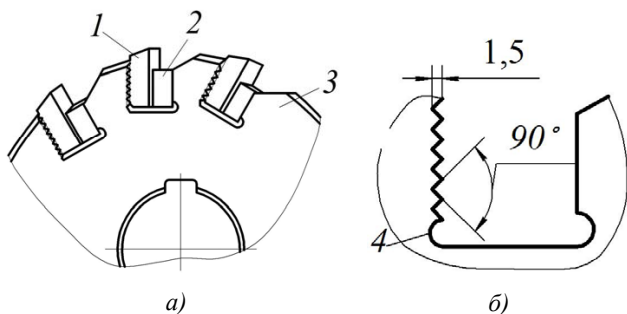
Сборная фреза (а), форма паза и размеры рифлений в корпусе фрезы (б): 1 – нож; 2 – клин; 3 – корпус; 4 – технологическая канавка
